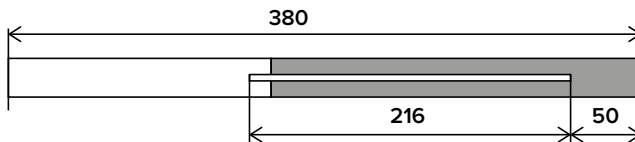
Прорези для беспроводного зонда MSt2 в сборе с адаптером под размер 380x32мм
